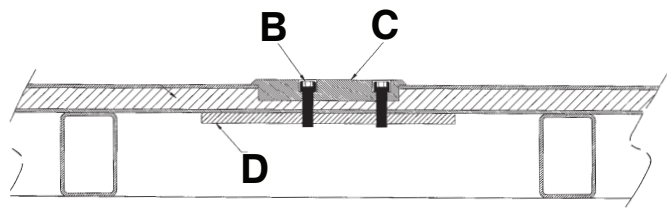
Anclaje de la placa de suelo en las aberturas empotradas
